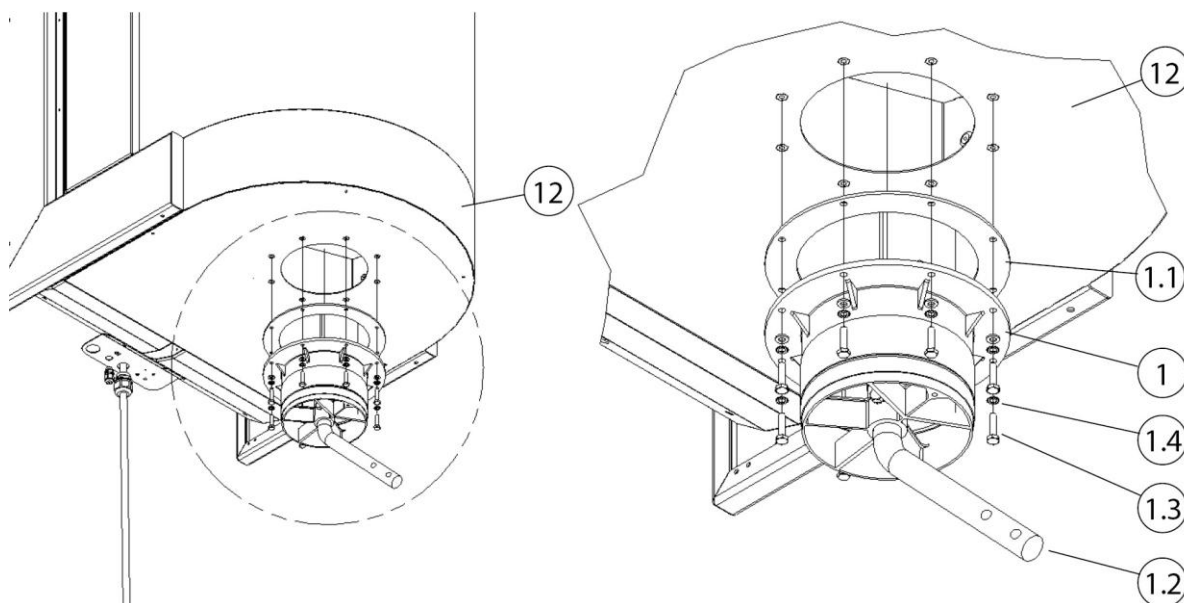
Montaje debajo de un equipo de filtrado fijo
